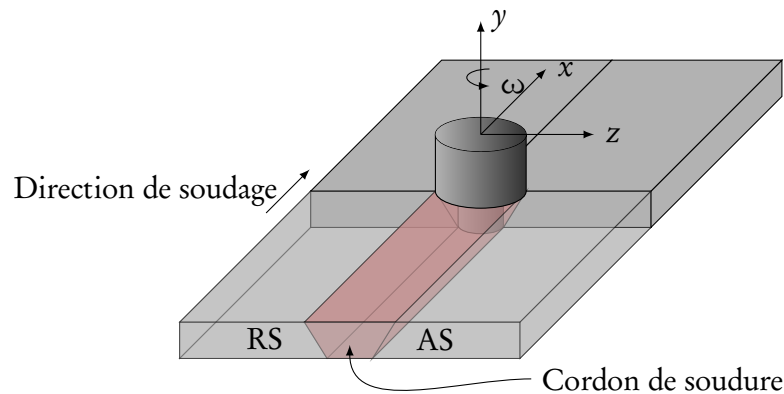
Schéma du procédé de soudage par friction malaxage.
